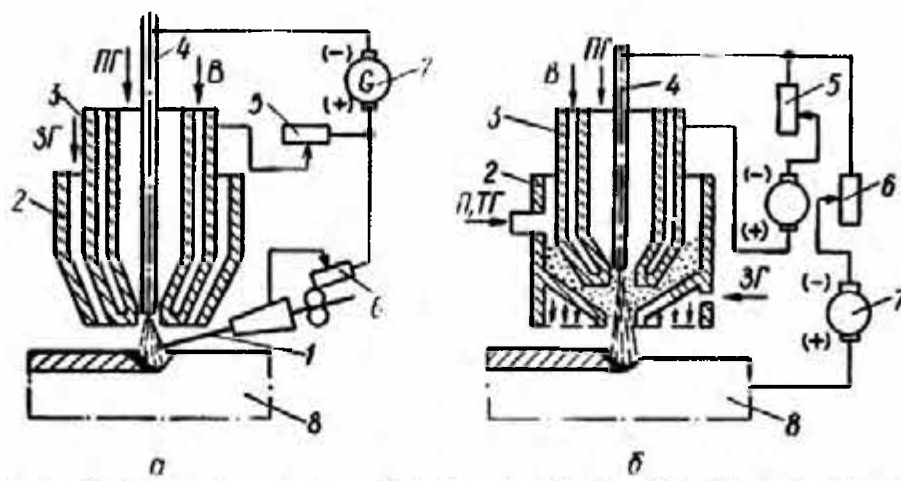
Схема плазмово-дугового напильювання присадним дротом (а) і металічним порошком (б): В – вода; ПГ – плазموутворювальний газ; ЗГ – захисний газ; П – транспортуючий газ; П – присадний порошок; 1 – присадний дріт; 2 – мундштук; 3 – сопло плазмового пальника; 4 – вольфрамовий електрод; 5, 6 – змінні опори; 7 – джерело струму; 8 – деталь.
